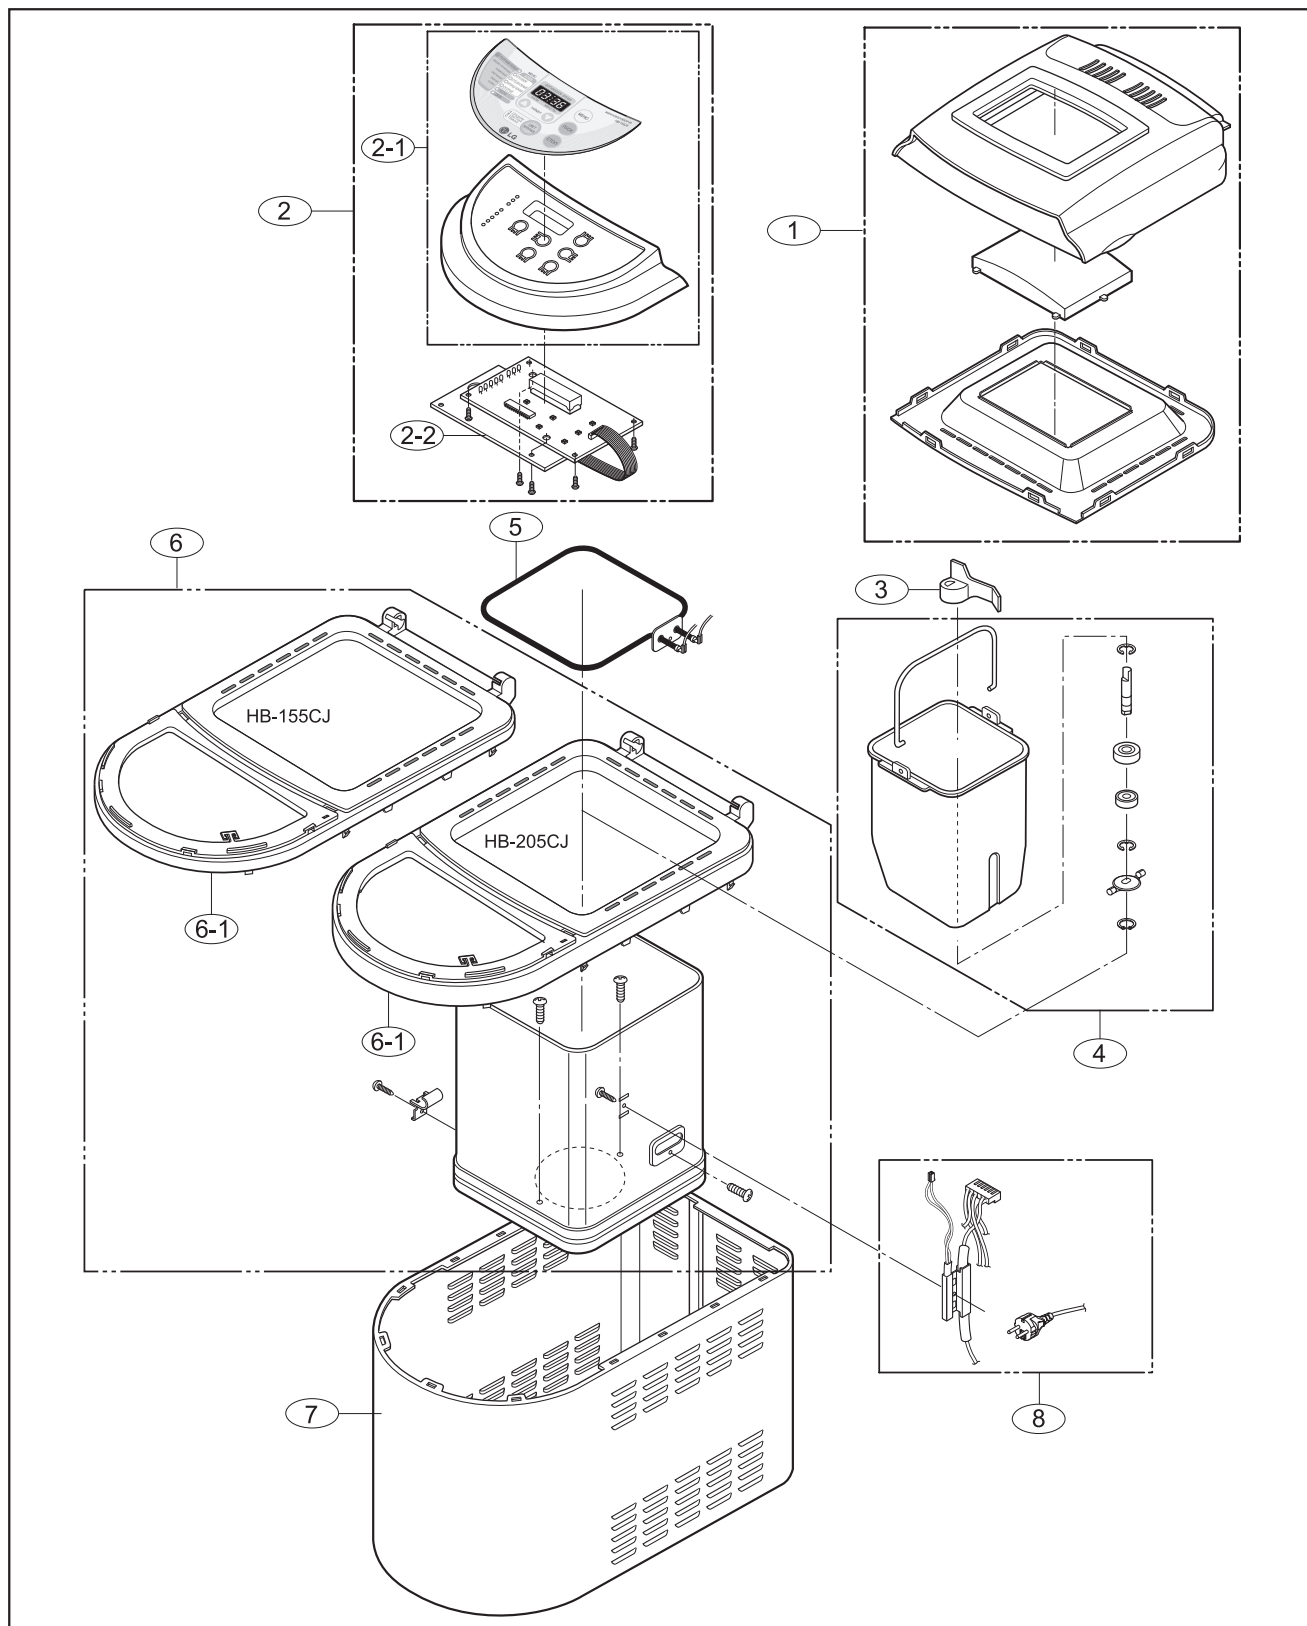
Сборочный чертеж хлебопечек (1), где: 1 – верхняя крышка, 2 – ПУ и ЭМ (2-1 – крышка ПУ; 2-2 – платы ПУ и ЭМ), 3 – лопатка, 4 – контейнер с валом лопатки, 5 – ТЭН, 6 – крышка с внутренним кожухом, 7 – внешний кожух, 8 – проводные соединители в сборе с датчиком температуры
